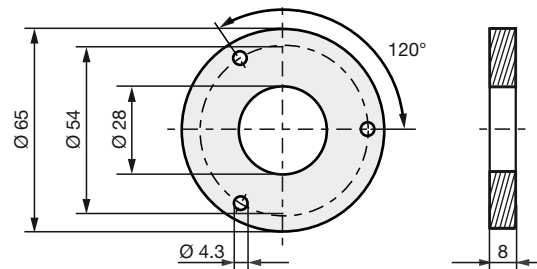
Accesorios especiales BTL-P-1028-15R
